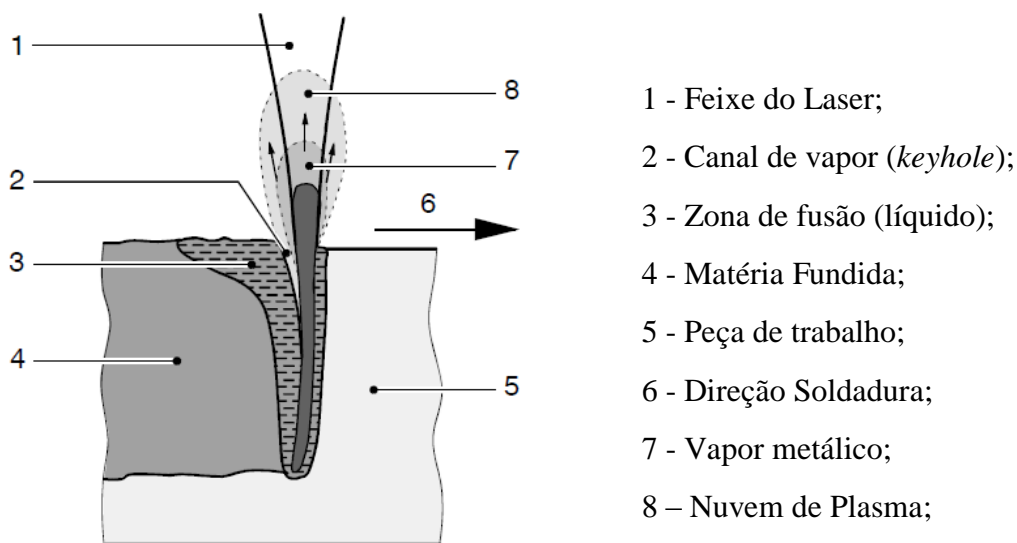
Princípio da soldadura profunda. ([TRUMPF Laser](#))
